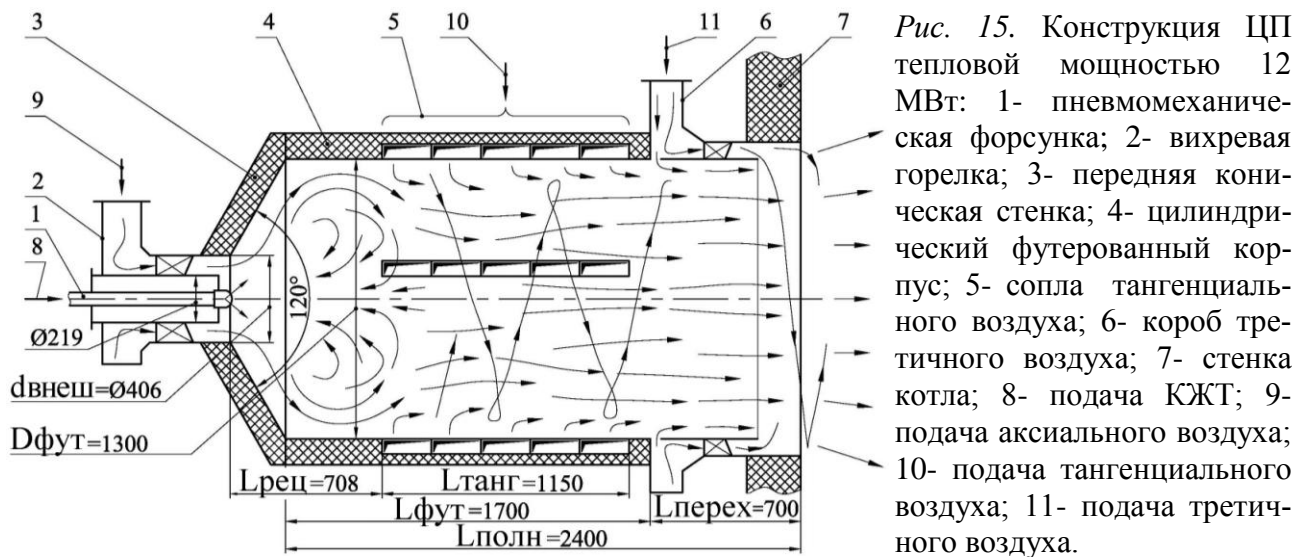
Конструкция ЦП тепловой мощностью 12 МВт: 1- пневмомеханическая форсунка; 2- вихревая горелка; 3- передняя коническая стенка; 4- цилиндрический футерованный корпус; 5- сопла тангенциального воздуха; 6- короб третичного воздуха; 7- стенка котла; 8- подача КЖТ; 9- подача аксиального воздуха; 10- подача тангенциального воздуха; 11- подача третичного воздуха.
